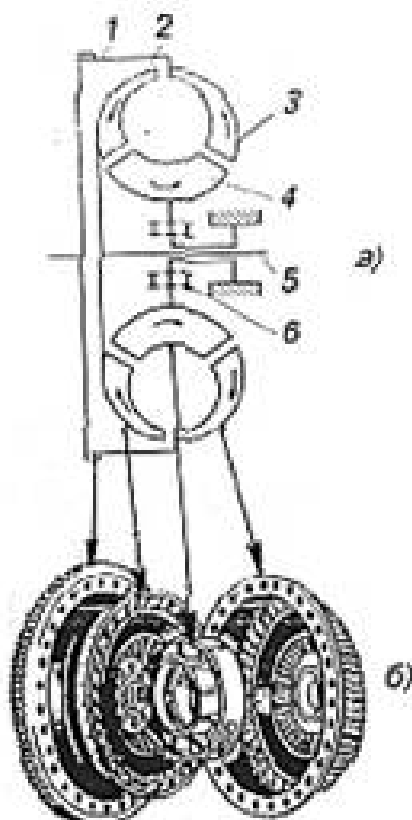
Гидротрансформатор: а – схема; б – в разобранном виде; 1 – маховик двигателя; 2 – турбинное колесо; 3 – насосное колесо; 4 – реактор; 5 – входной вал КП; 6 – обгонная муфта
